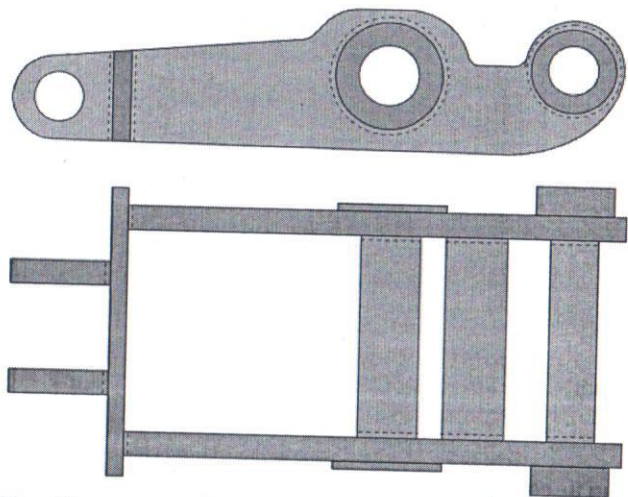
Контроль околошовных зон сварных соединений втулок и торцевой соединительной планки с боковинами рычага и кронштейнов с торцевой соединительной планкой
